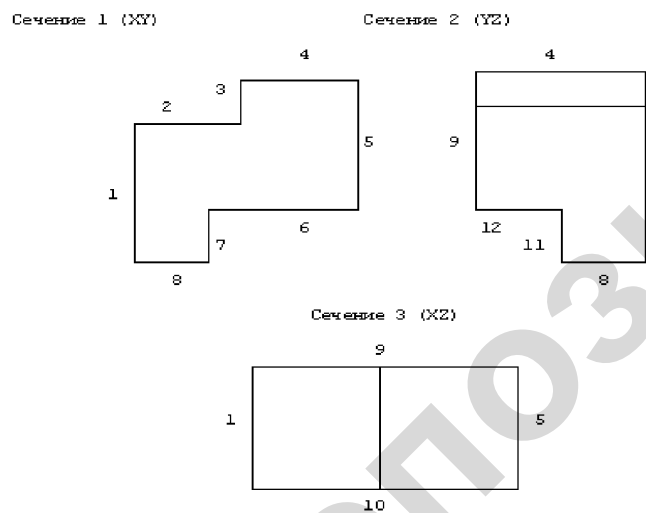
Пример обозначения поверхностей контура плоской детали
